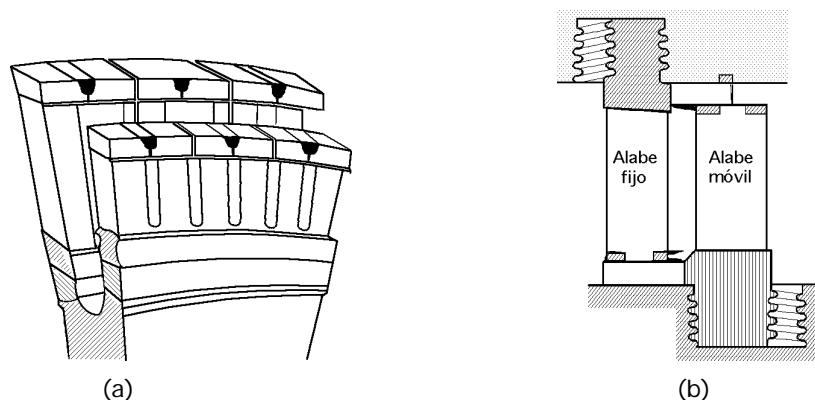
Fijación y montaje en la base: (a) por soldadura; (b) por diente de sierra
